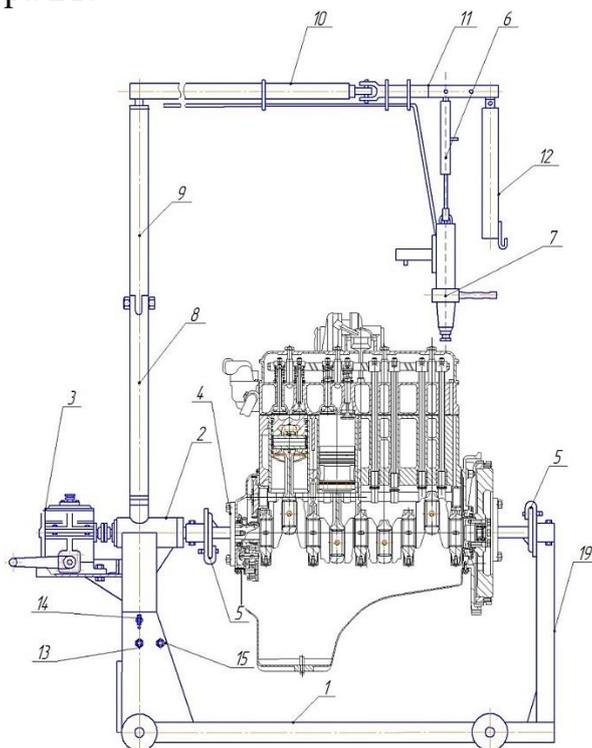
Стенд для разборки и сборки двигателей: 1 – основание;
